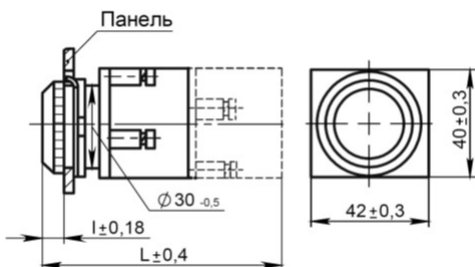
Габаритные размеры выключателей с цилиндрическим толкателем
